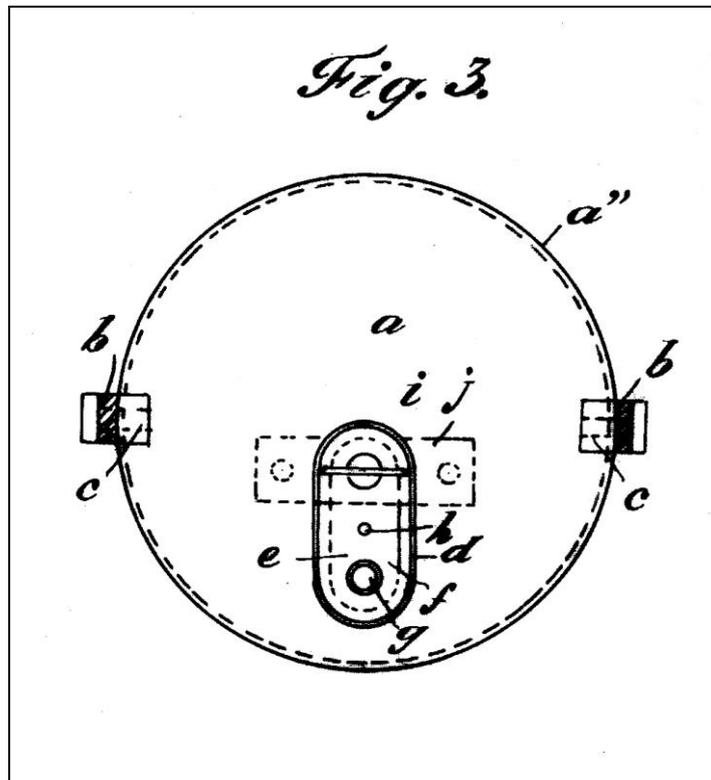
Plano superior (Arch. J.M. Sanchis)
